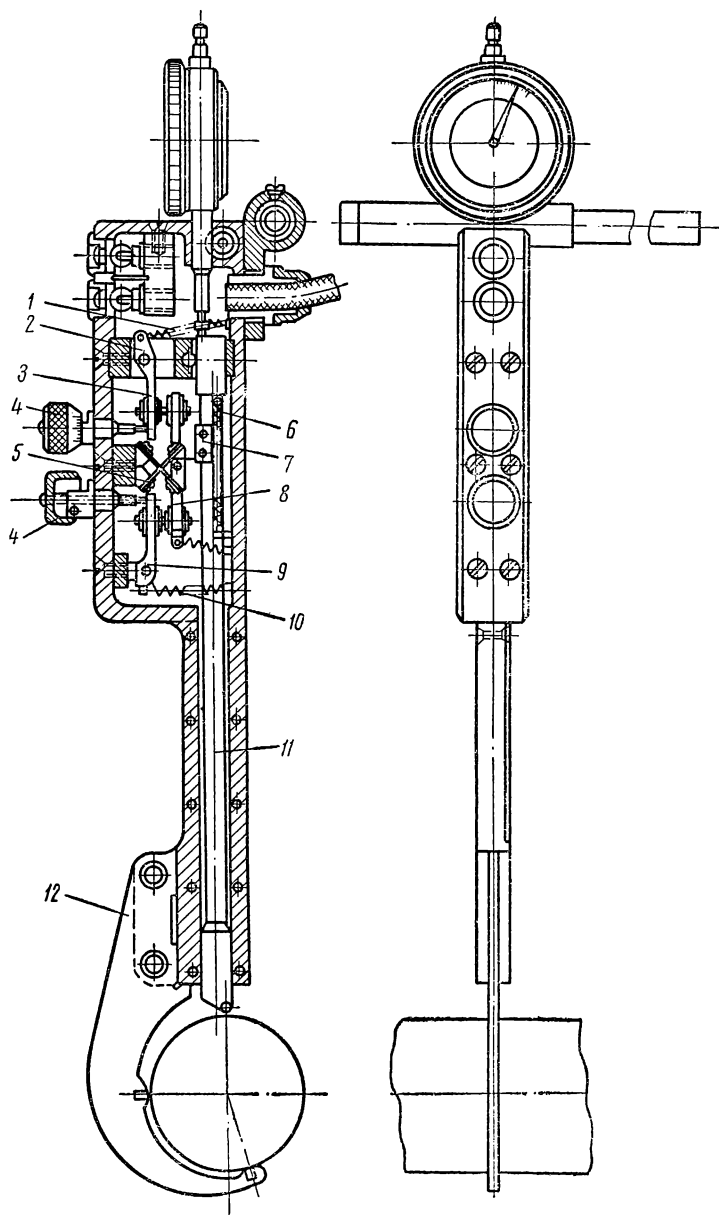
Устройство для автоматического контроля шлифуемой детали
